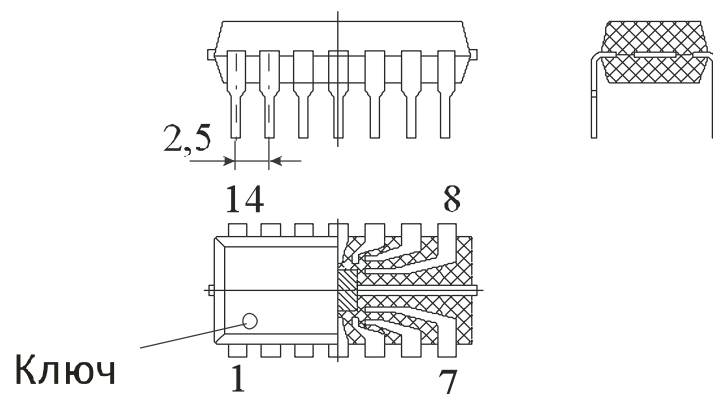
Конструкція пластмасового корпусу 2102
